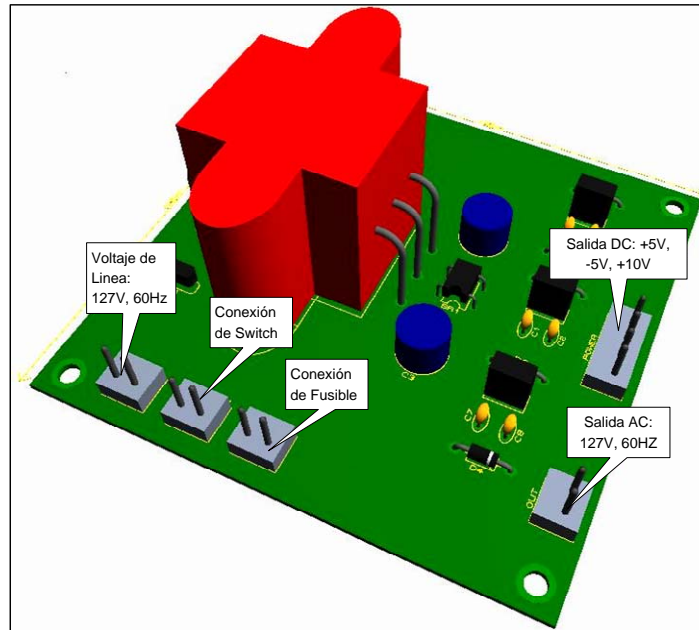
Aspecto en tres dimensiones de la PCB de la Fuente de Alimentación.
